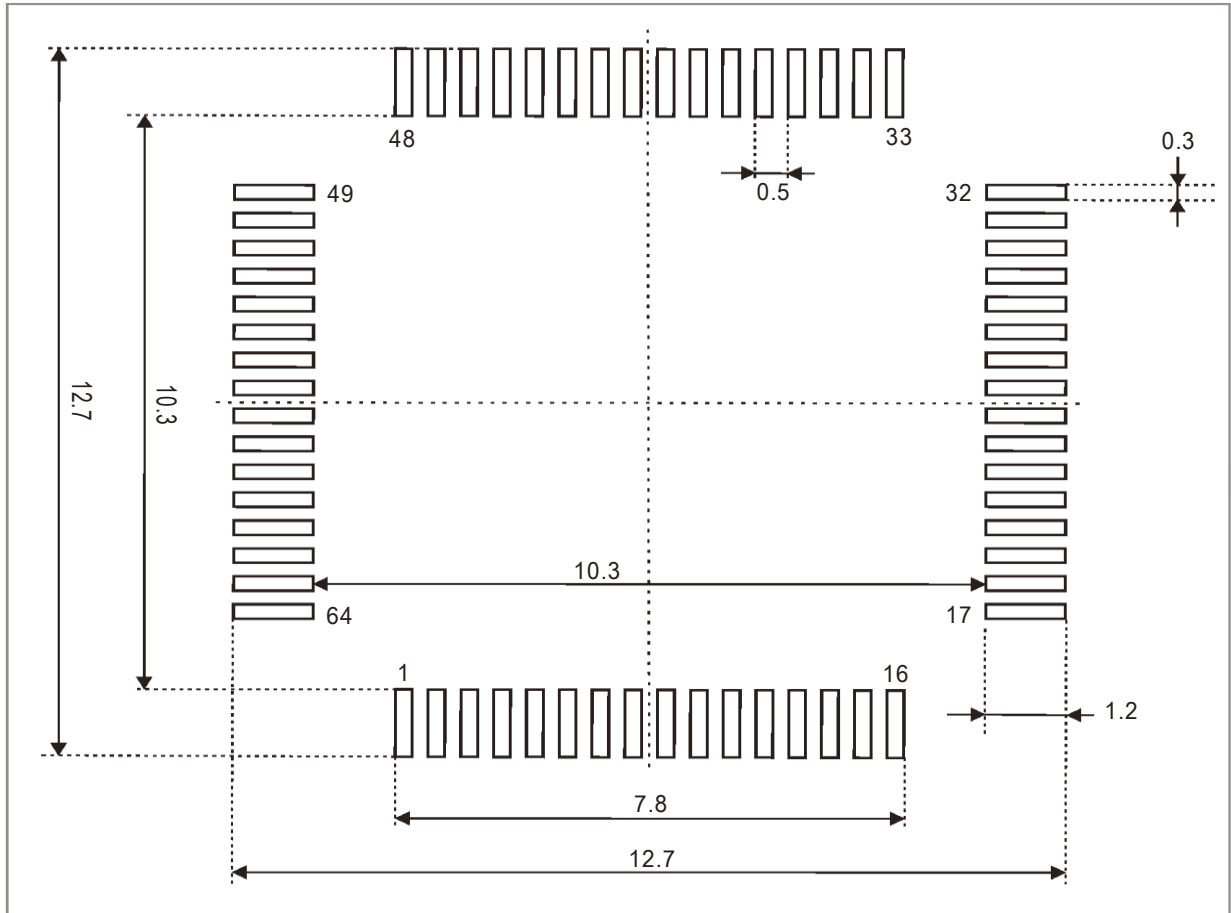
LQFP64 芯片的 PCB 安装尺寸图
